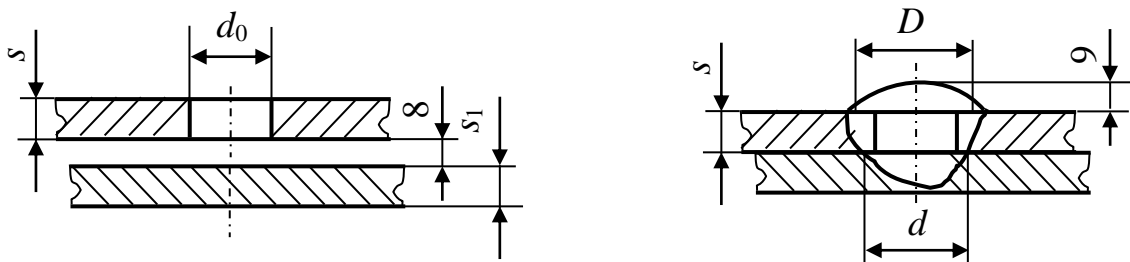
Зварний шов № 1, з'єднання Н5
